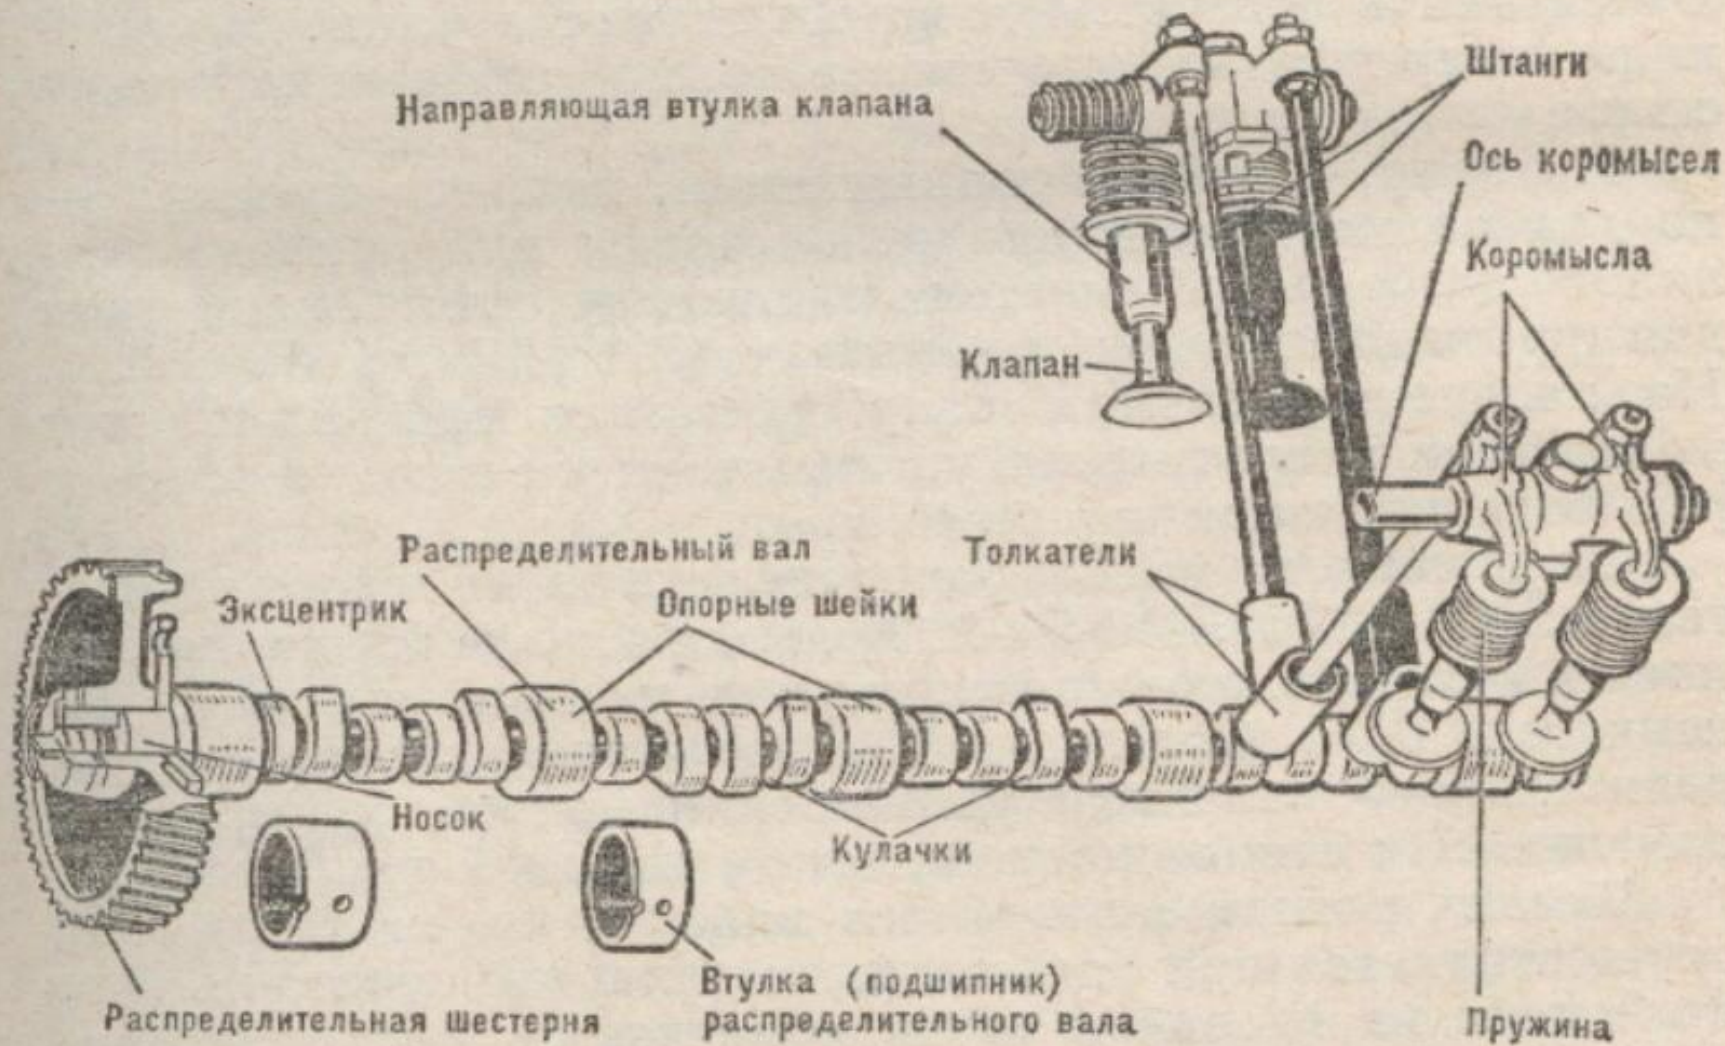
Газораспределительный механизм двигателя ЗИЛ-130
